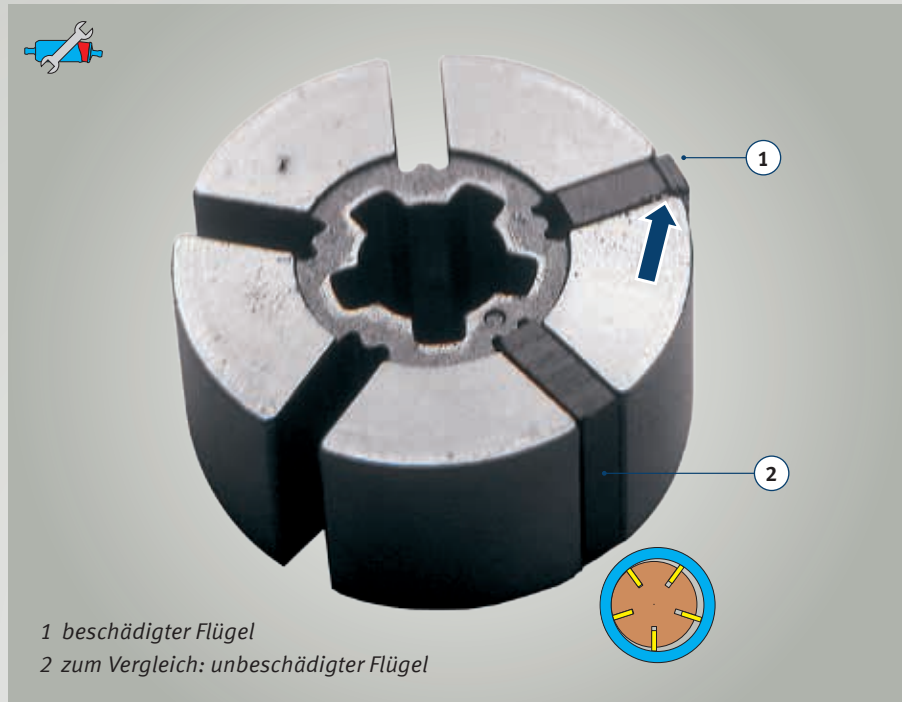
Pumpenwerk einer Flügelzellenpumpe – Schaden durch Fremdkörper
